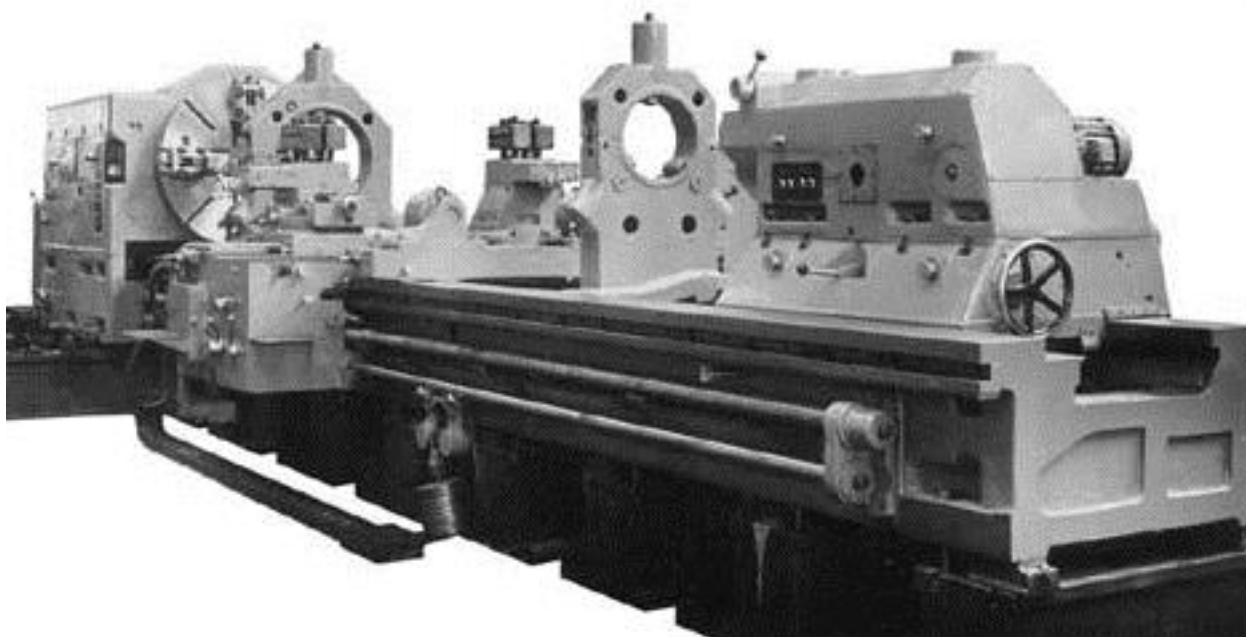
Металорізальний верстат моделі 1А660Ф3
